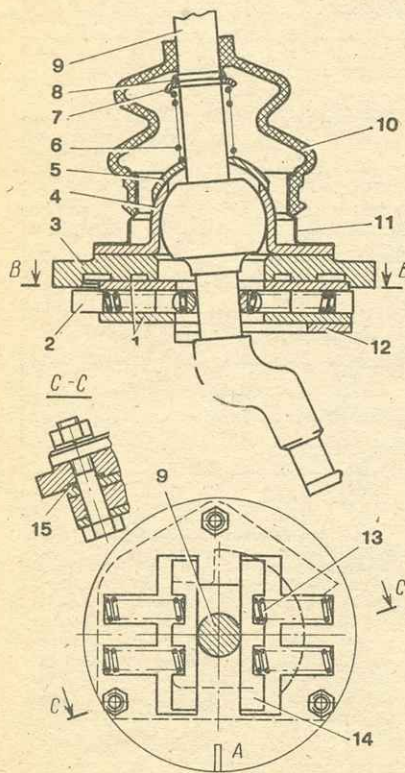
Механизм выбора передач: 1 — шайбы направляющей пластины; 2 — направляющая пластина; 3 — корпус рычага переключения передач; 4 — шаровая опора рычага; 5 — сферическая шайба; 6 — пружина; 7 — упорное кольцо; 8 — стопорное кольцо; 9 — рычаг переключения передач; 10 — защитный чехол; 11 — фланец; 12 — блокирующая скоба заднего хода; 13 — пружина; 14 — направляющая планка; 15 — уплотнительное кольцо; А — риска.
